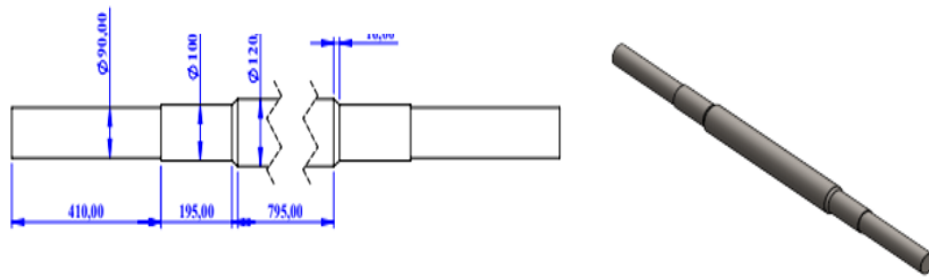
Conjunto Rolo Soldado - Torque Rolo Soldado
